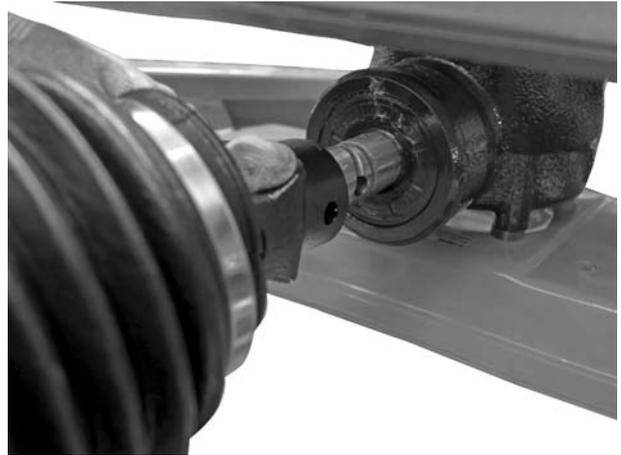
Надевание карданного вала на конец вала редуктора
